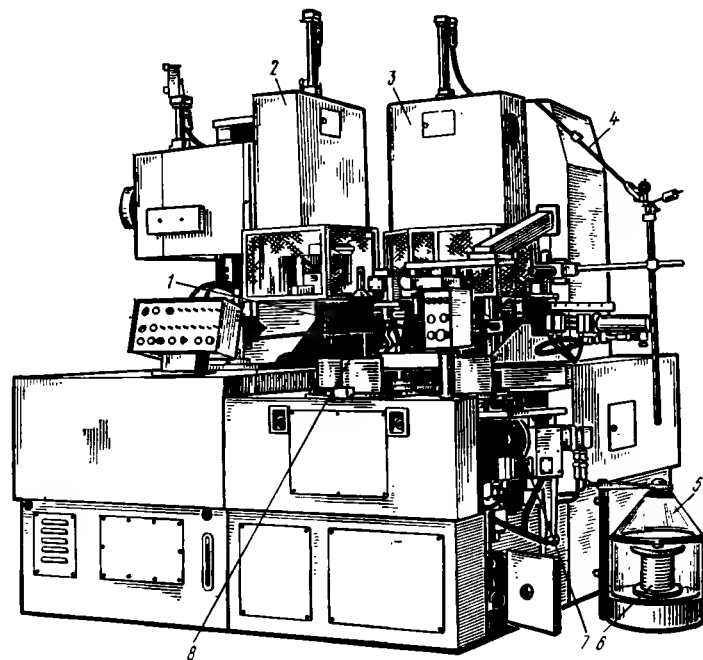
Агрегатный станок АНВС для обмотки статоров:
